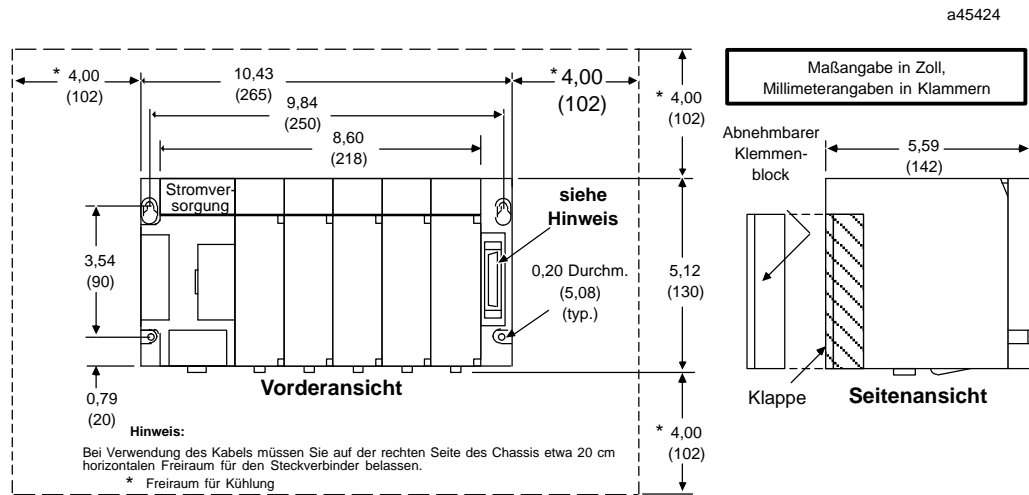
Einbaumaße eines Chassis mit 5 Steckplätzen
